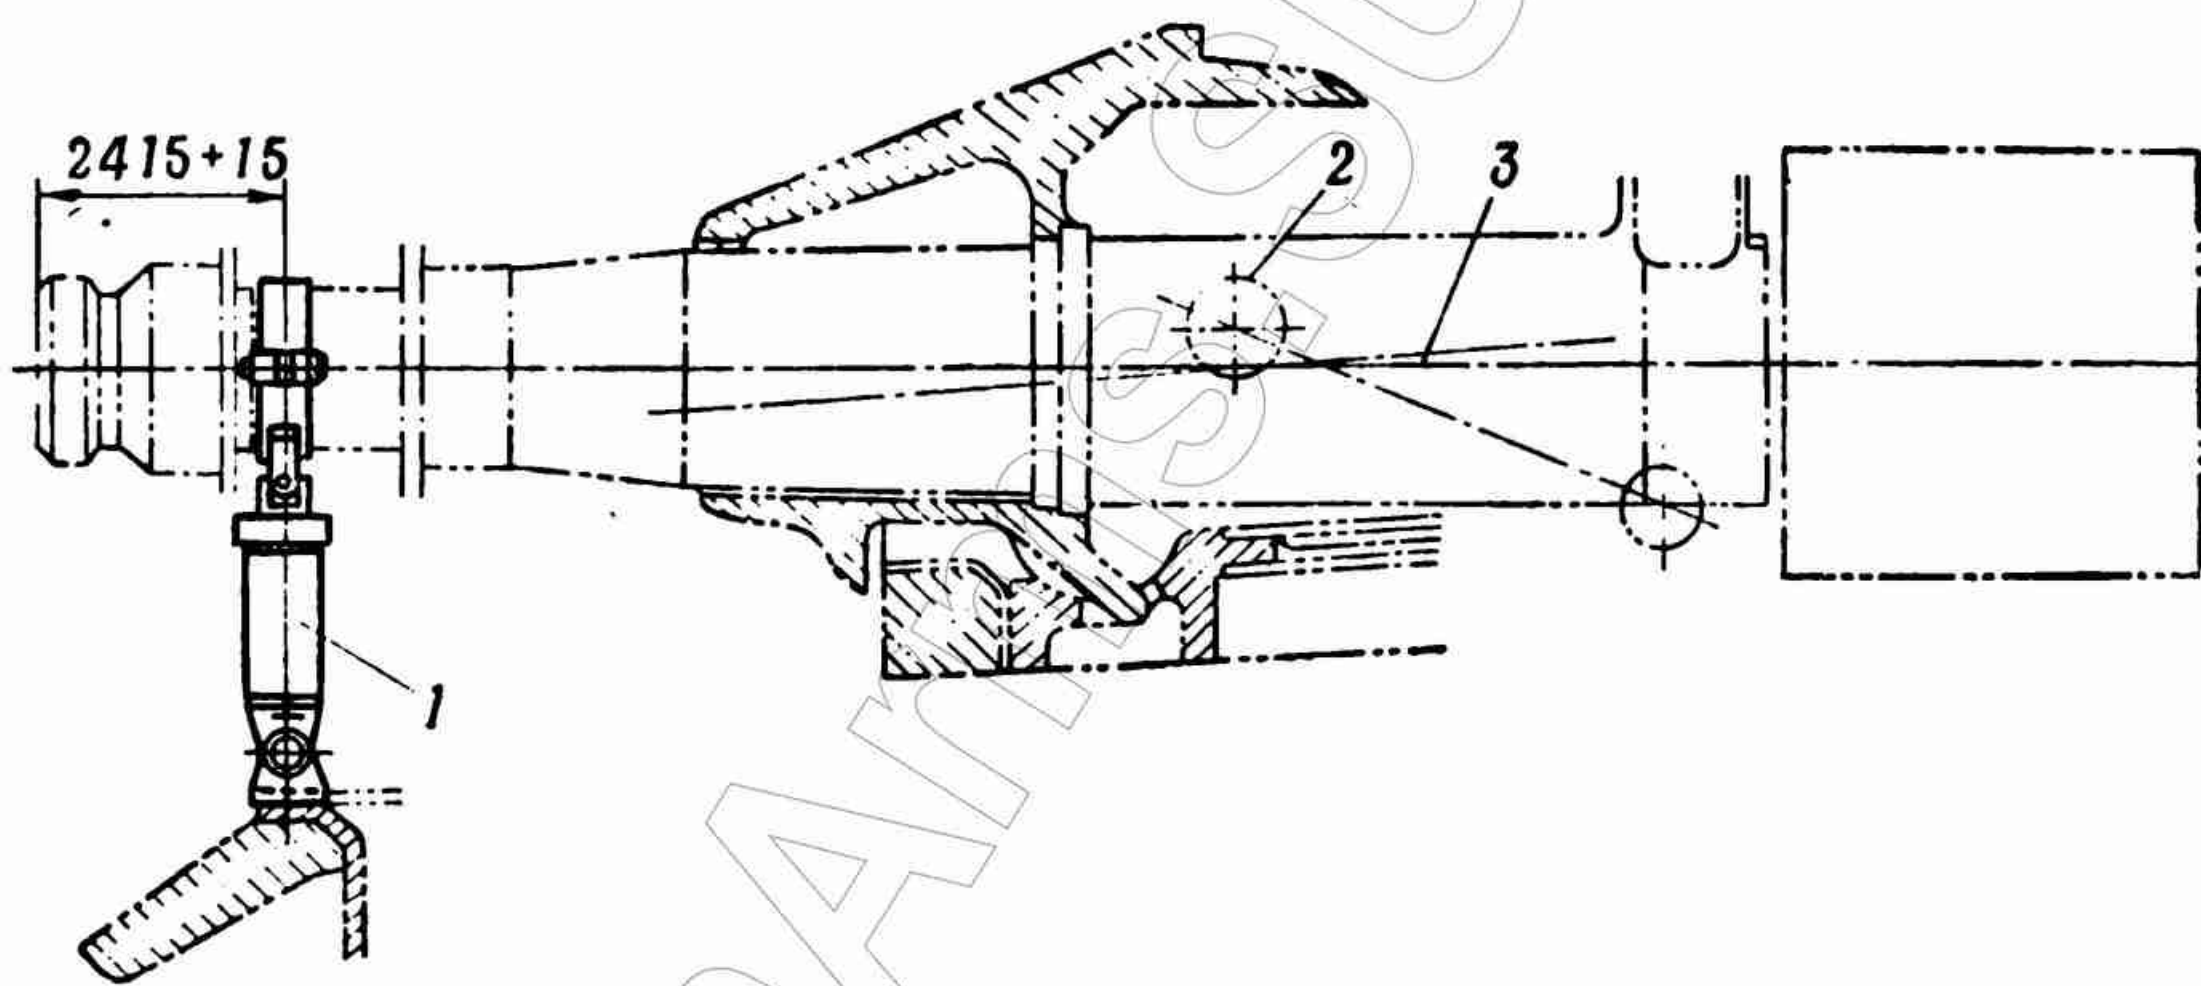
Схема установки прибора для проверки момента фрикциона:
